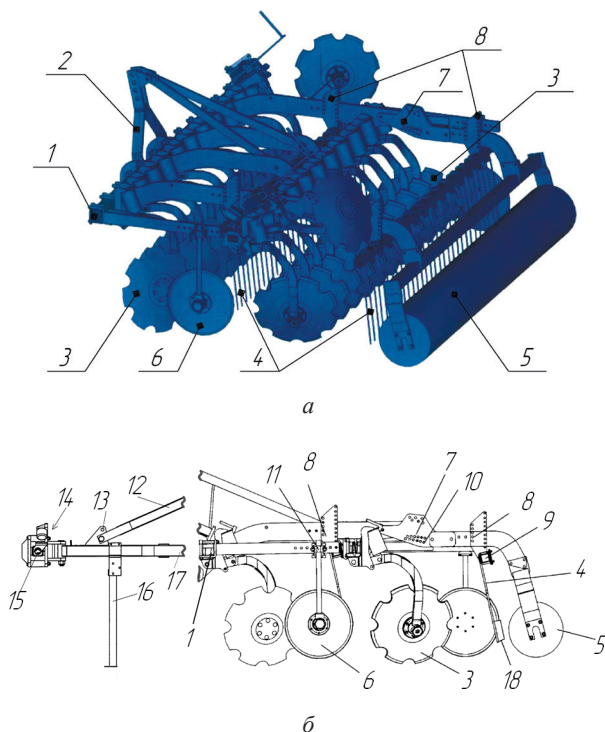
Схема дисковых почвообрабатывающих агрегатов:
